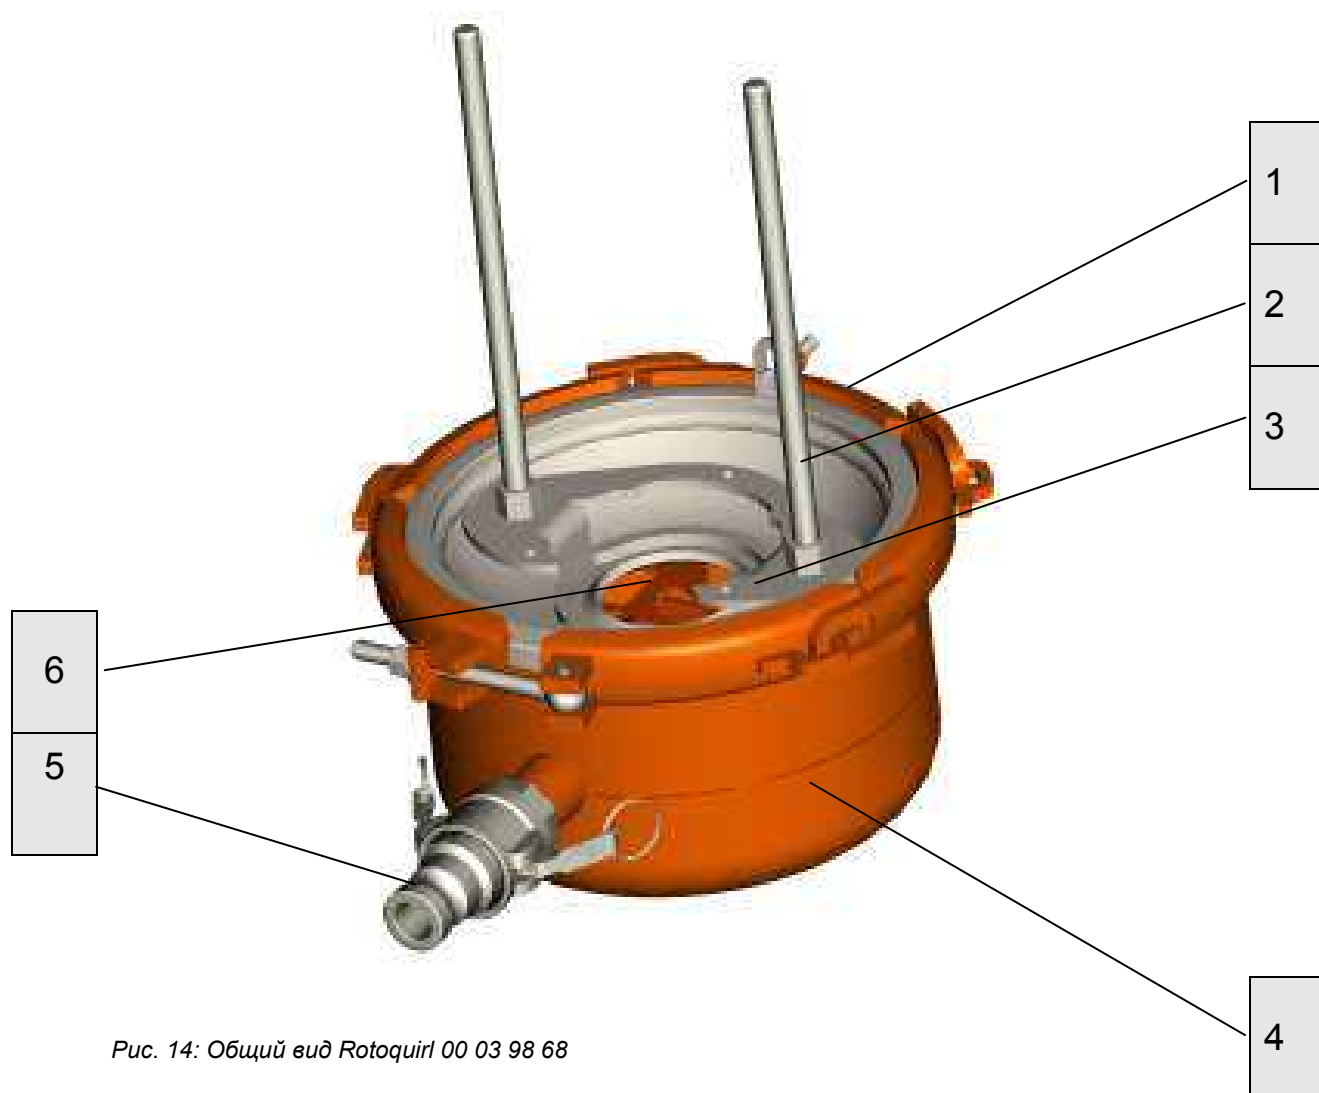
Общий вид Rotoquirл 00 03 98 68
